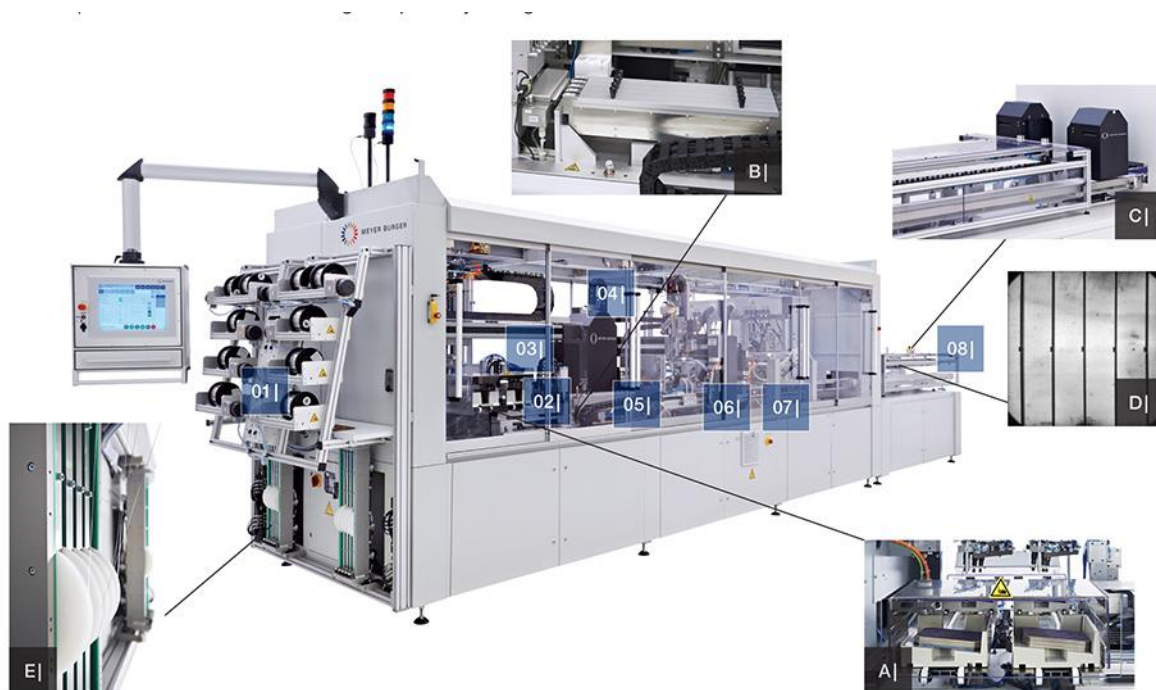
Máquina de soldadura de celdas en string. Imagen ilustrativa. Tomado de (Solarview, 2021)
